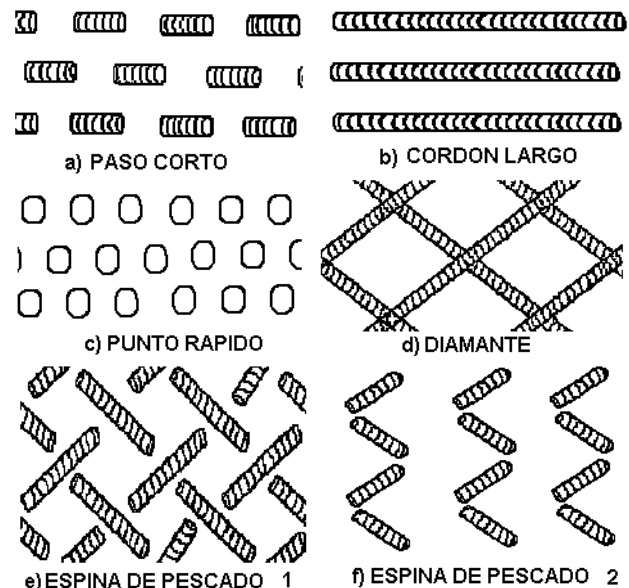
Algunos tipos de cordones de soldadura. [12]
